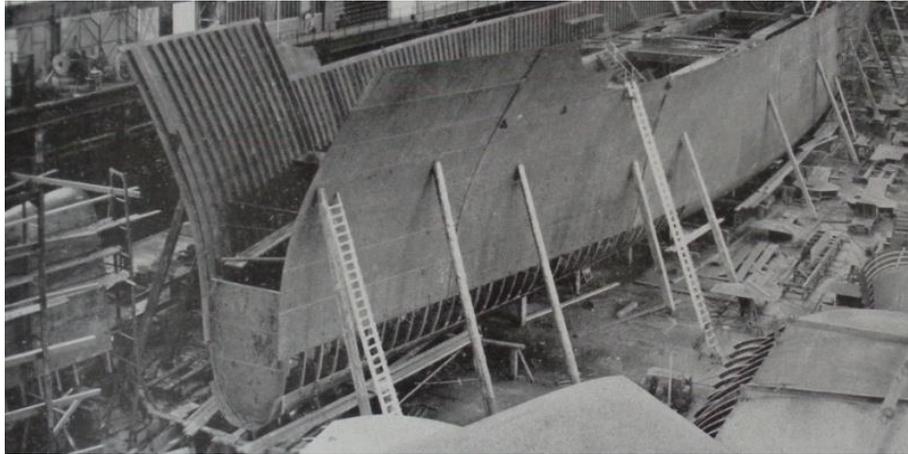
Le *Cambraisien* en attente d'exécution des joints soudés
